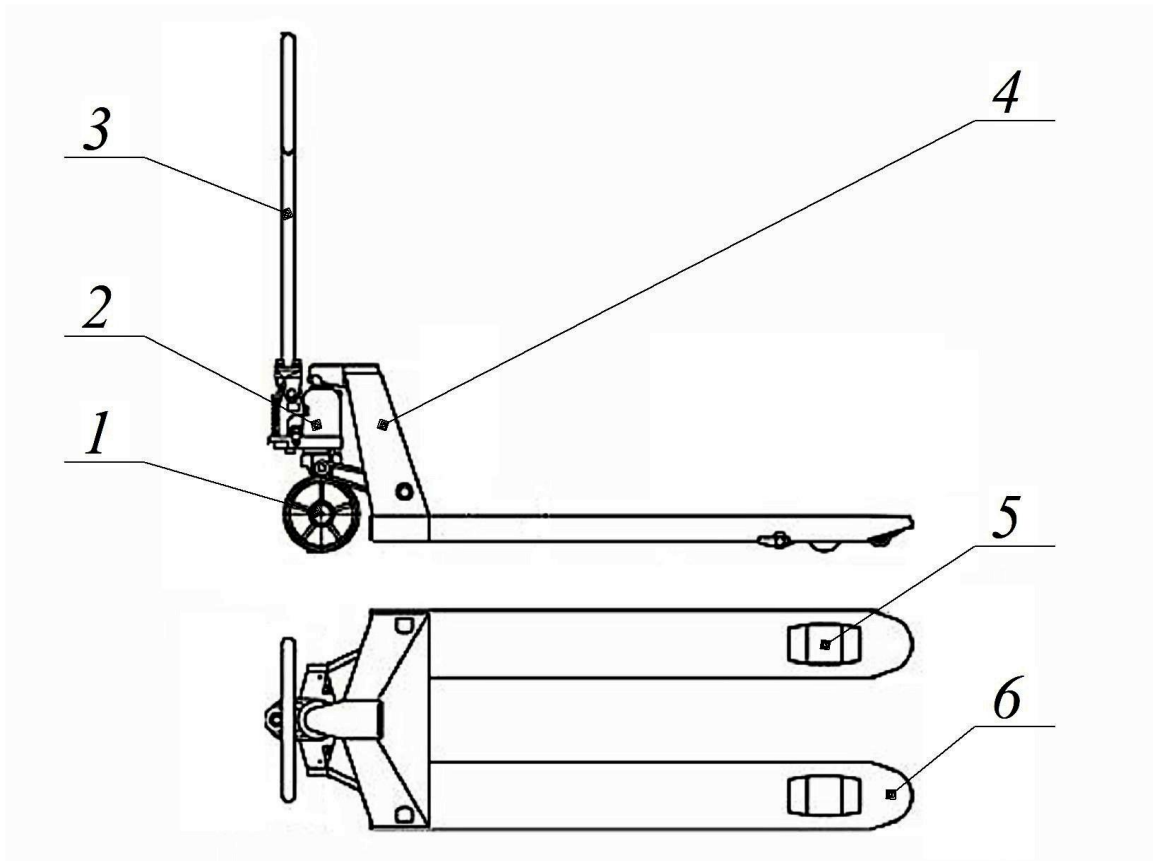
Ручний несамохідний візок з підйомними вилами:
